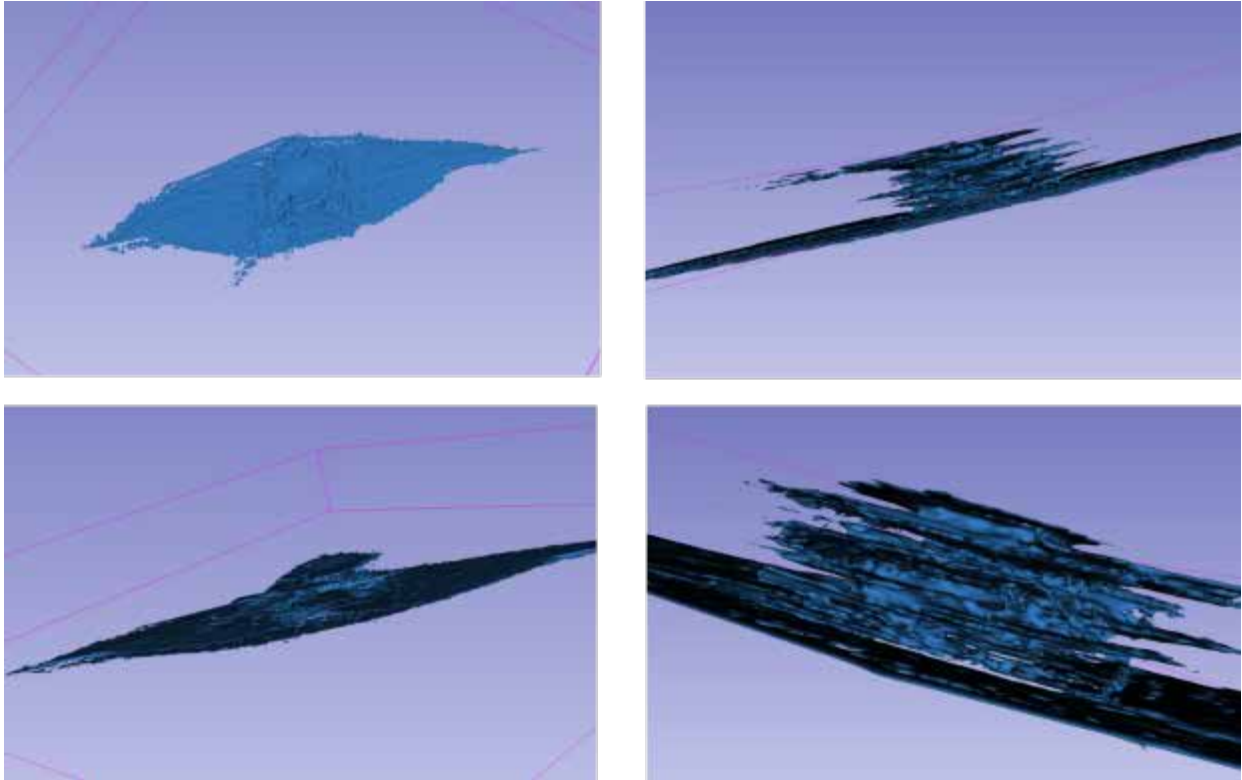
Reconstruction tridimensionnelle des surfaces délaminées au sein d'une plaque fabriquée à partir du préimprégné M21/T700 impactée à 24 J.
